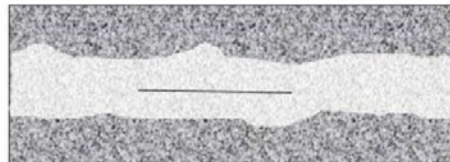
Falta de Fusión, en el medio de la pared de soldadura.
